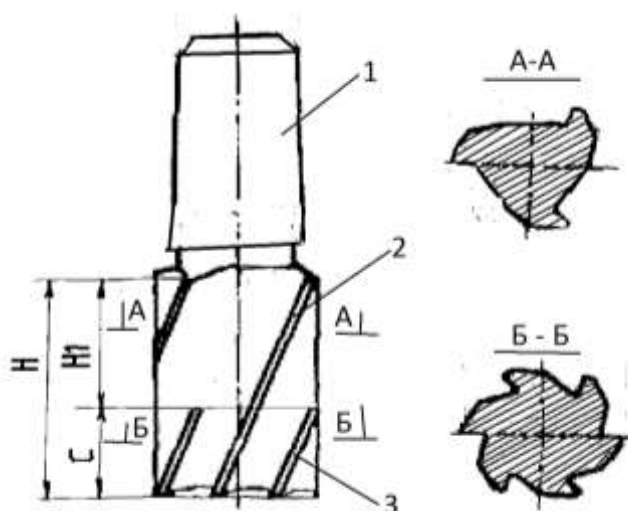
концевая фреза с дополнительными зубьями в торцовой части.
